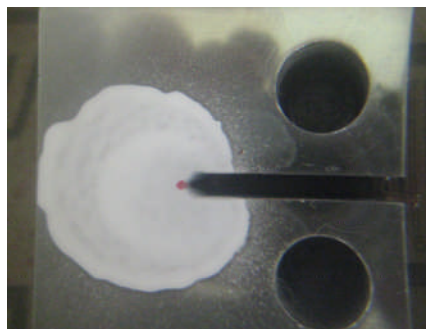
Revelado de la grieta por tintas penetrantes
